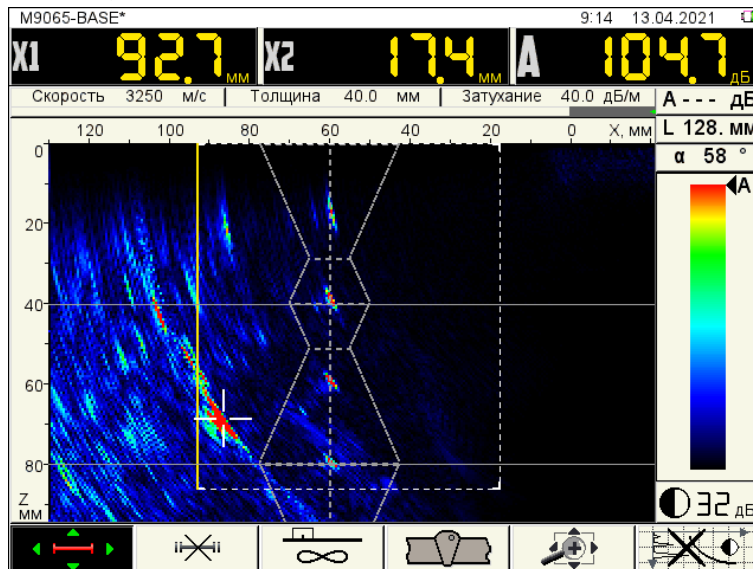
Установленная зона контроля и маска сварного шва
